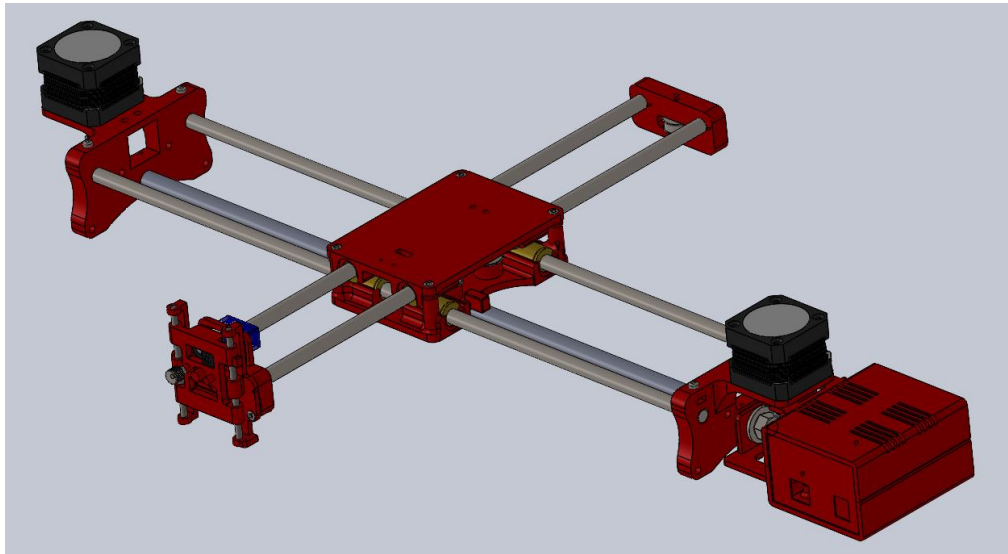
3D-модель базової конструкції двокоординатного плотера
